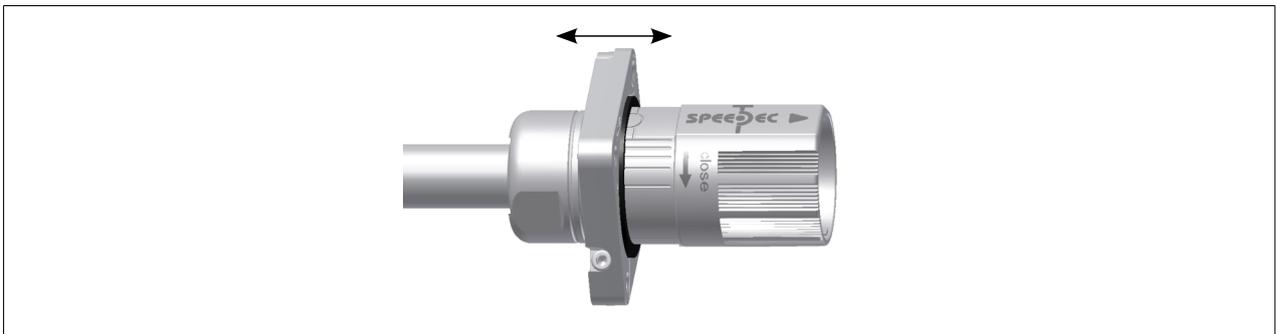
Metallflansch an Stecker anbringen (Hinterwandmontage)
